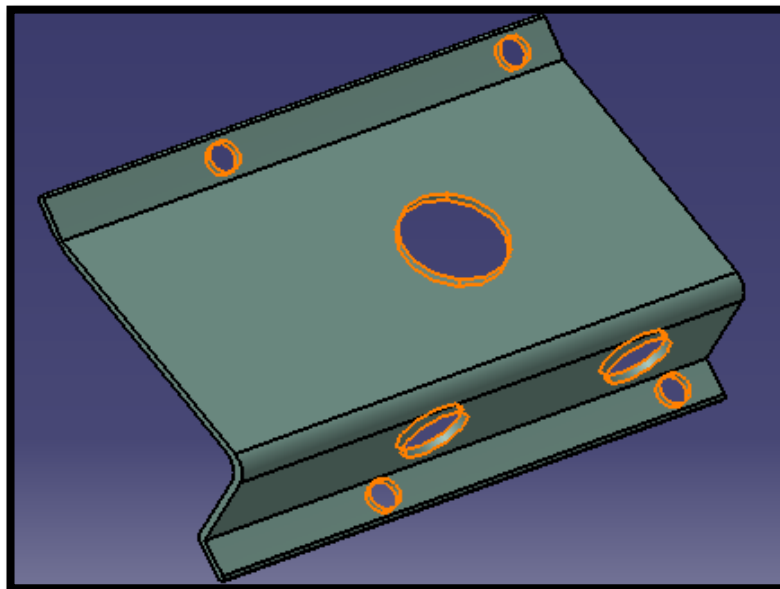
Seat mounting frame 11: Holes sujeción inferior 2
